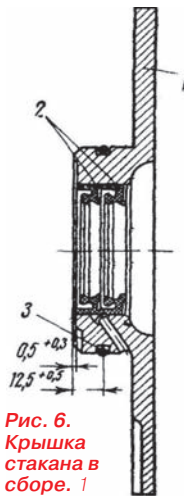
Крышка стакана в сборе. 1 — крышка; 2 — уплотнительная манжета; 3 — уплотнительное кольцо.
